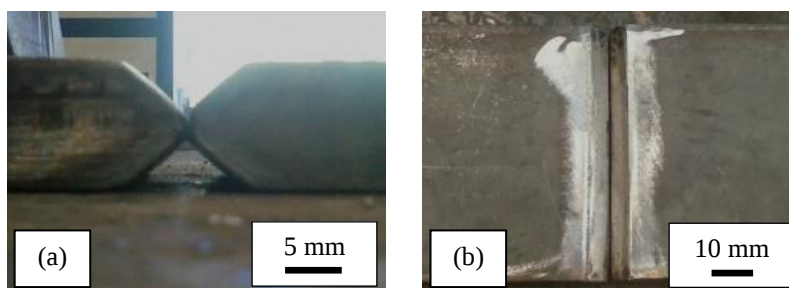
(a) Secção transversal de uma junta com chanfro tipo “duplo V” usinado; (b) junta em posição para os recebimentos dos cordões de solda.
